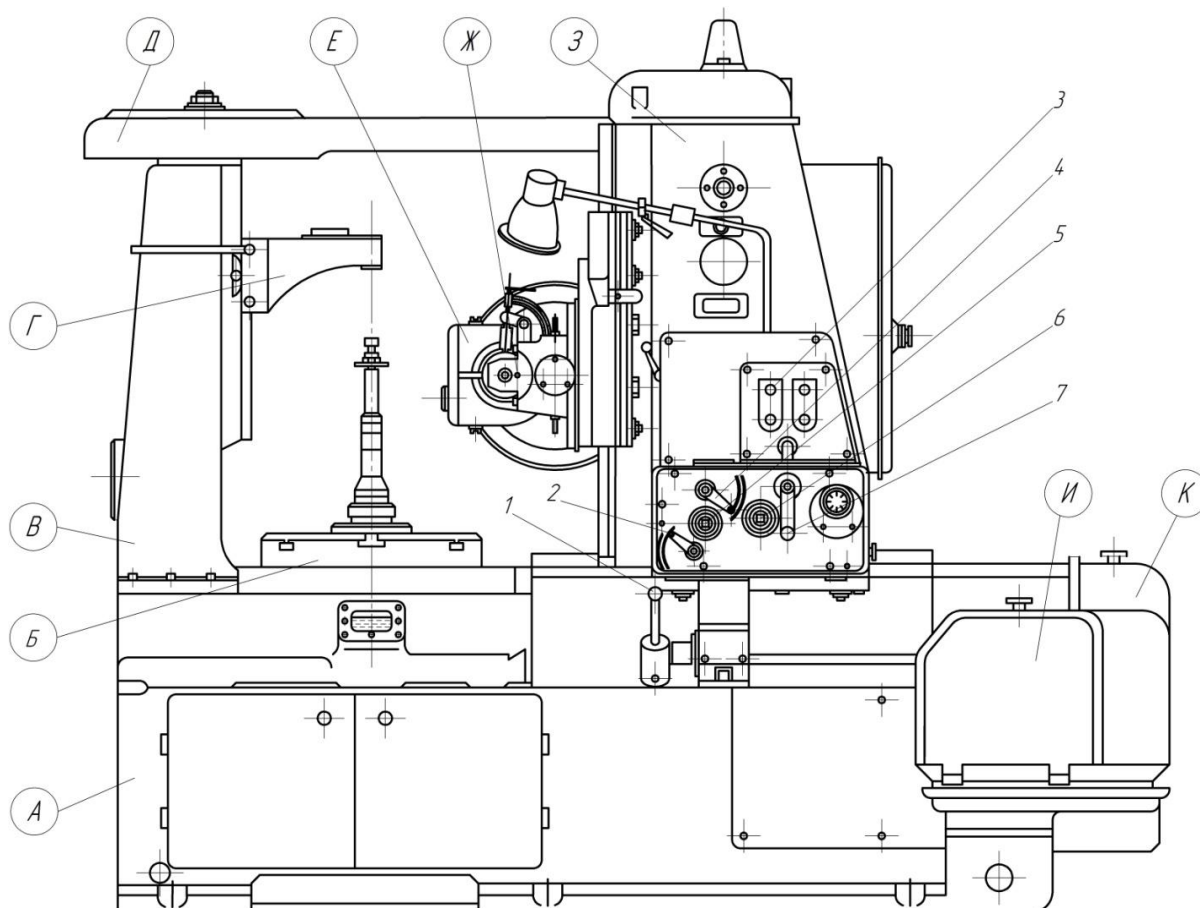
Общий вид зубофрезерного полуавтомата модели 5Д32. Основные узлы станка:
